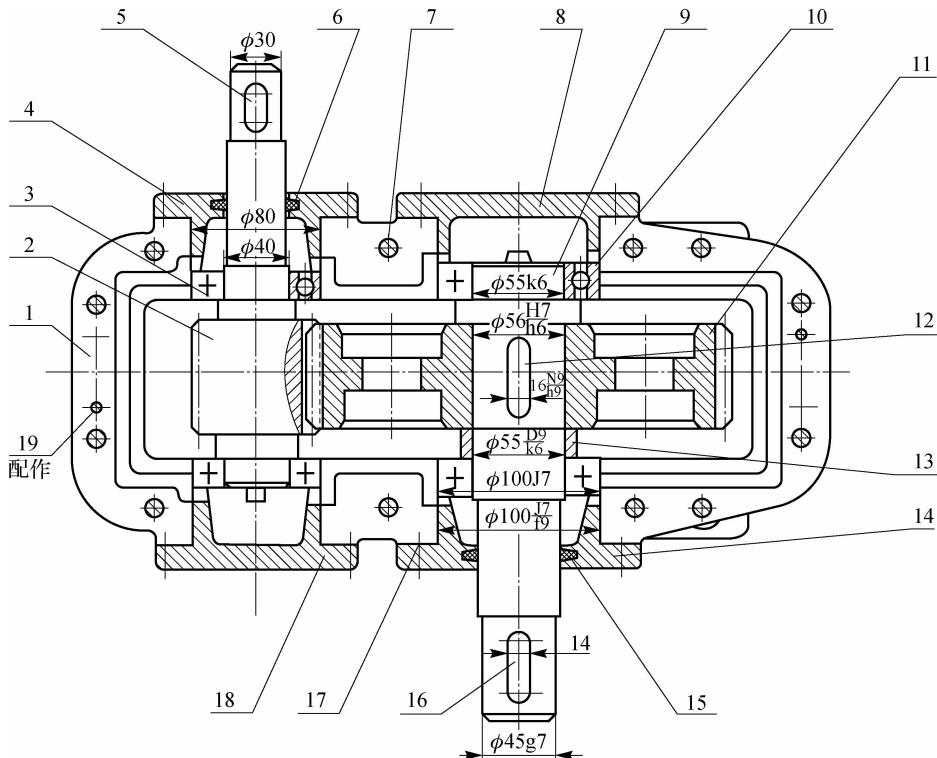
齿轮减速器的结构示意图(从结合面剖分的俯视剖视图)
